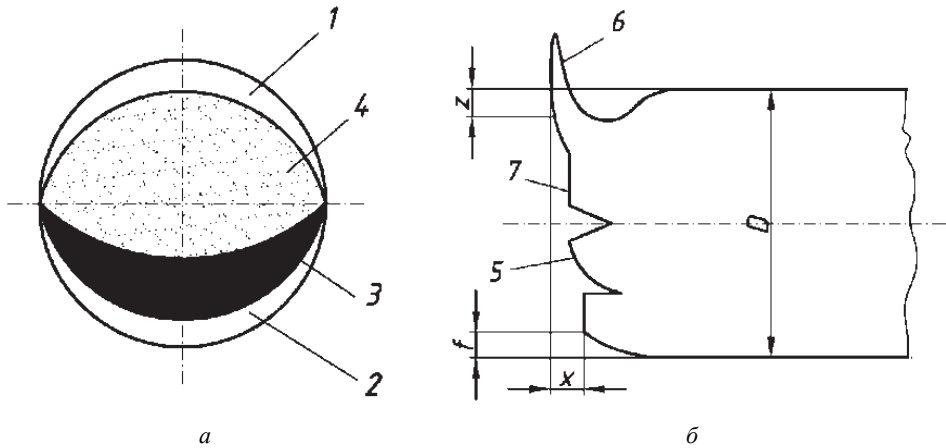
Схемы торцевой поверхности отрезанной заготовки при нормальном (а) и увеличенном (б) зазорах: 1 – зона смятия металла; 2 – зона утяжки металла; 3 – зона внедрения ножей и среза металла; 4 – зона скола металла; 5 – торцевые трещины; 6 – заусенец; 7 – скол; D – диаметр заготовки; z – увеличенное смятие; x – косина среза сверх установленной нормы; f – увеличенная утяжка
